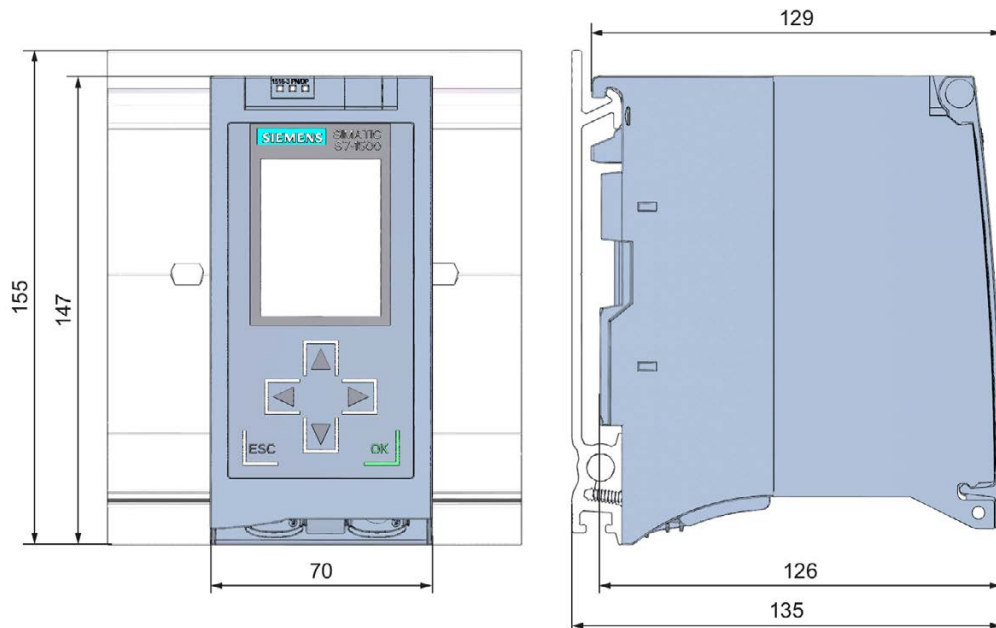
Maßbild der CPU 1516-3 PN/DP, Front- und Seitenansicht
